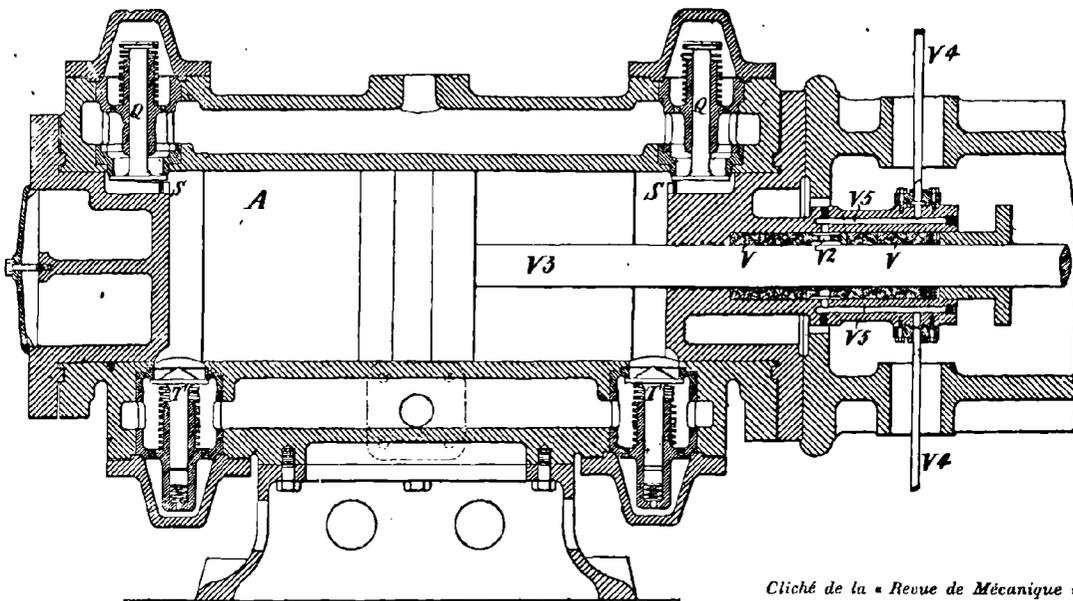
Piston de compresseurs à AzH_3 ou à SO_2 .
